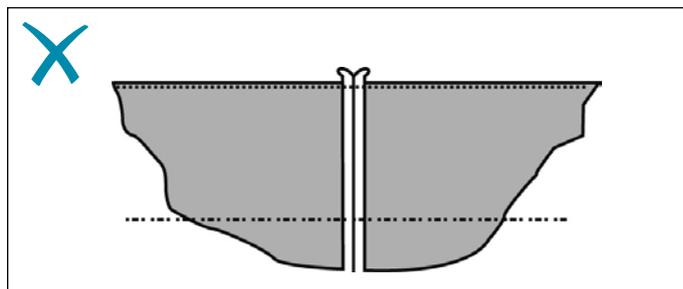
Ligne de soudure (défectueuse)
